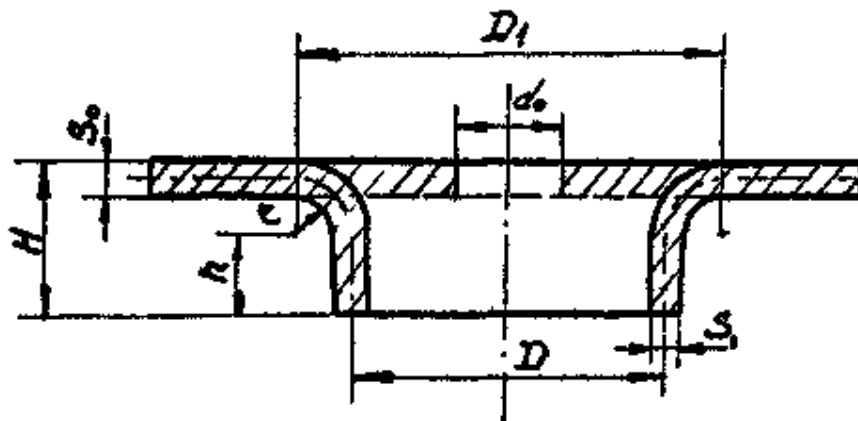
Размеры заготовки и детали при отбортовке.
